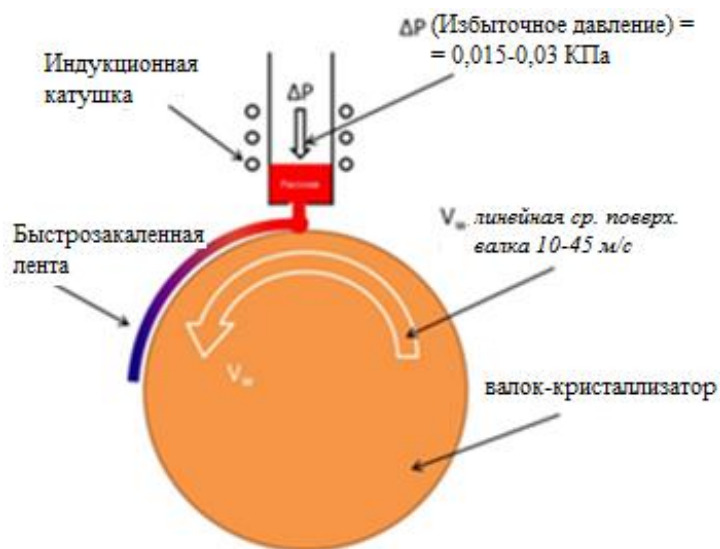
Установка спиннингования расплава в вакууме Dexing Magnet Tech. Melt Spinner Machine DX-11
